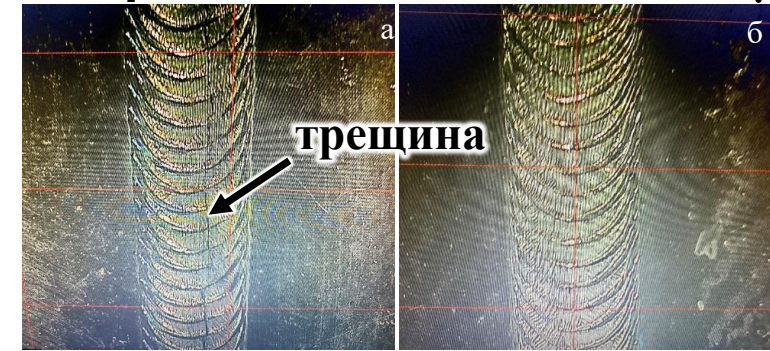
Внешний вид сварных соединений из сплава на основе γ -TiAl, полученных без предварительного подогрева (а) и с подогревом (б) импульсной лазерной сваркой
